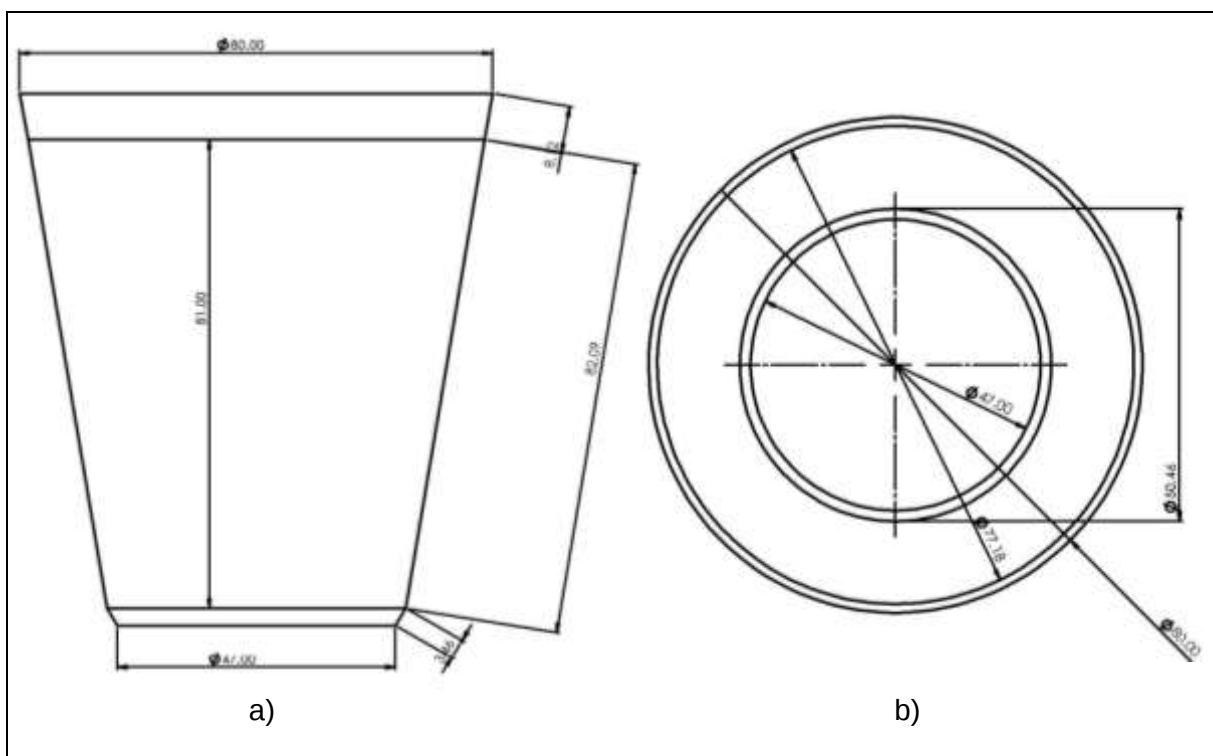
Dimensiones principales de la pieza en mm, a) vista lateral y b) base superior e inferior.
